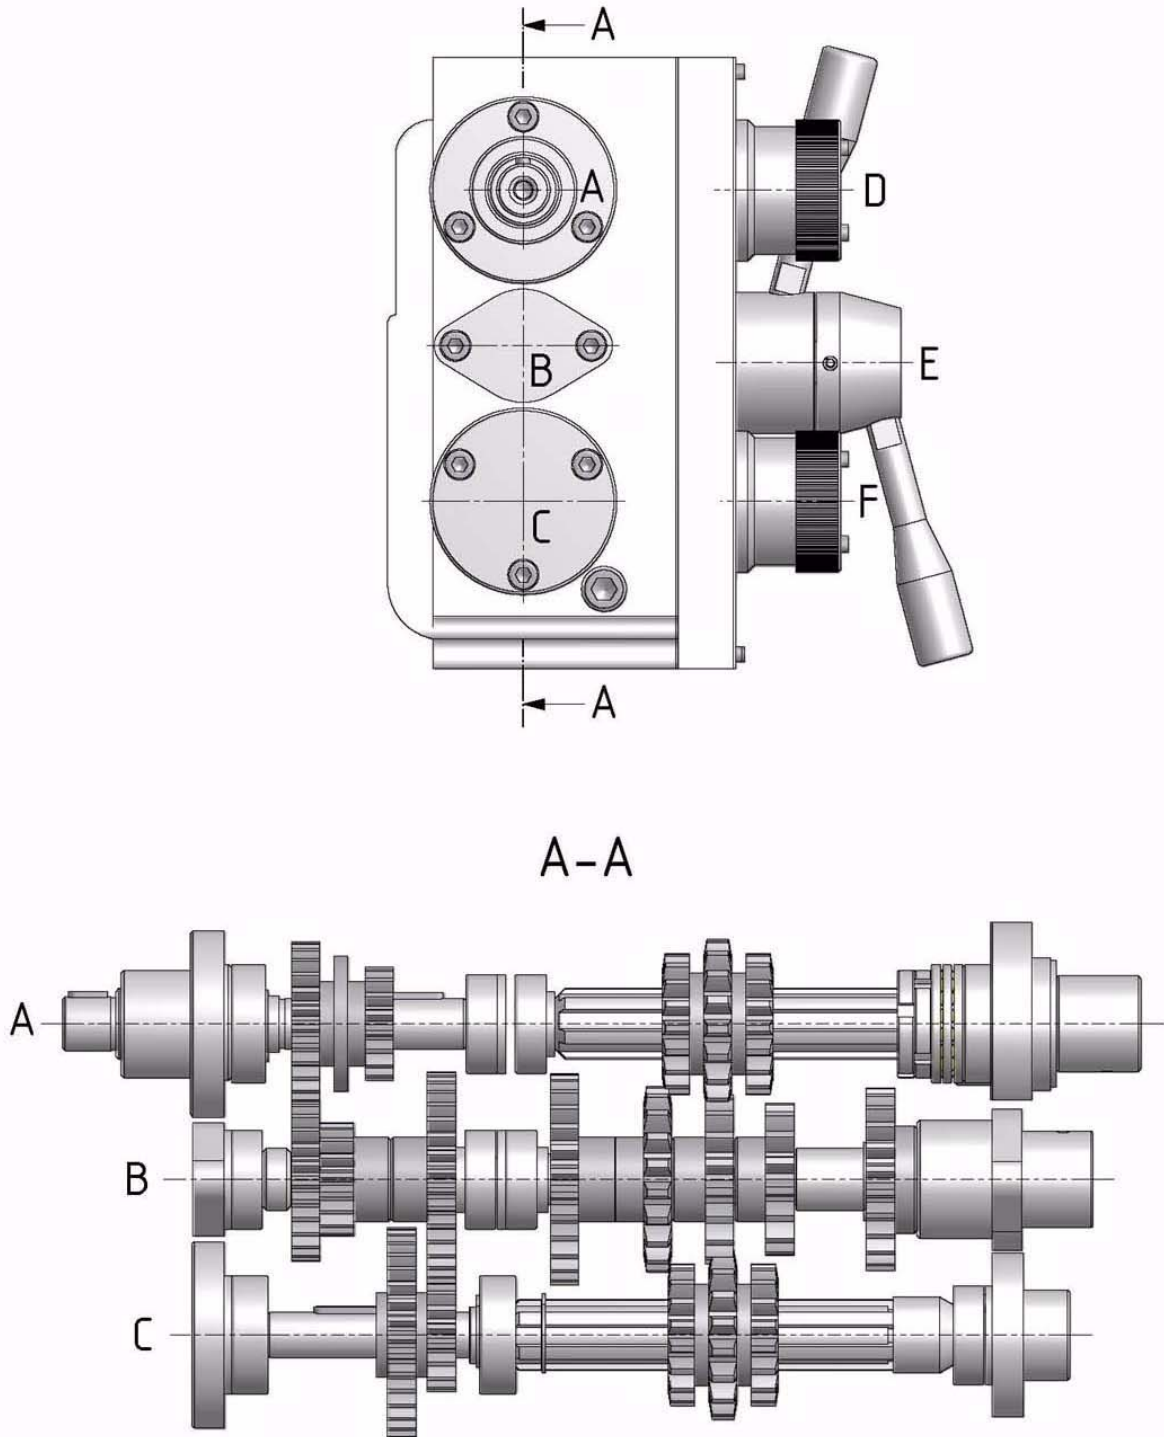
Vorschubgetriebe 1-4 - Feed gear 1-4
